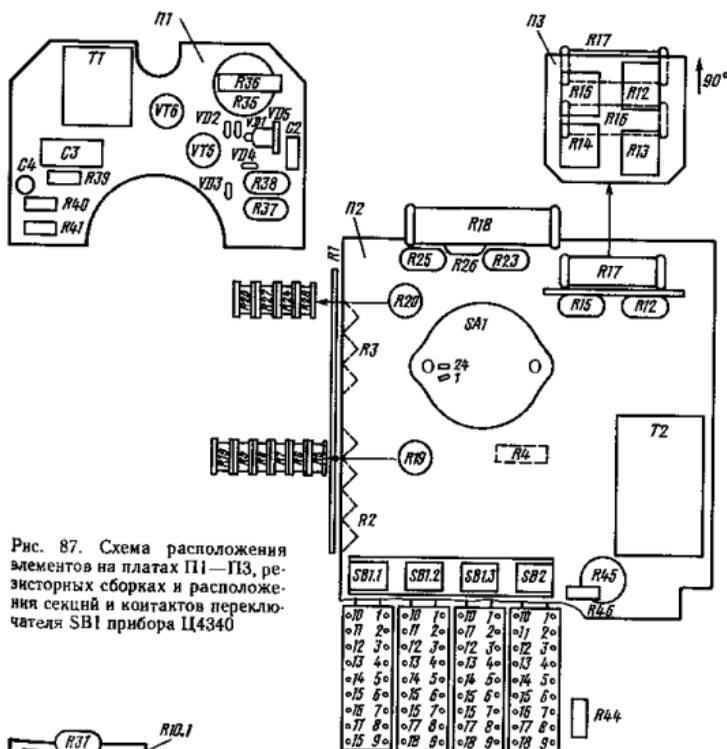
Схема расположения элементов на платах П1—П3, резисторных сборках и расположении секций и контактов переключателя SB1 прибора Ц4340
